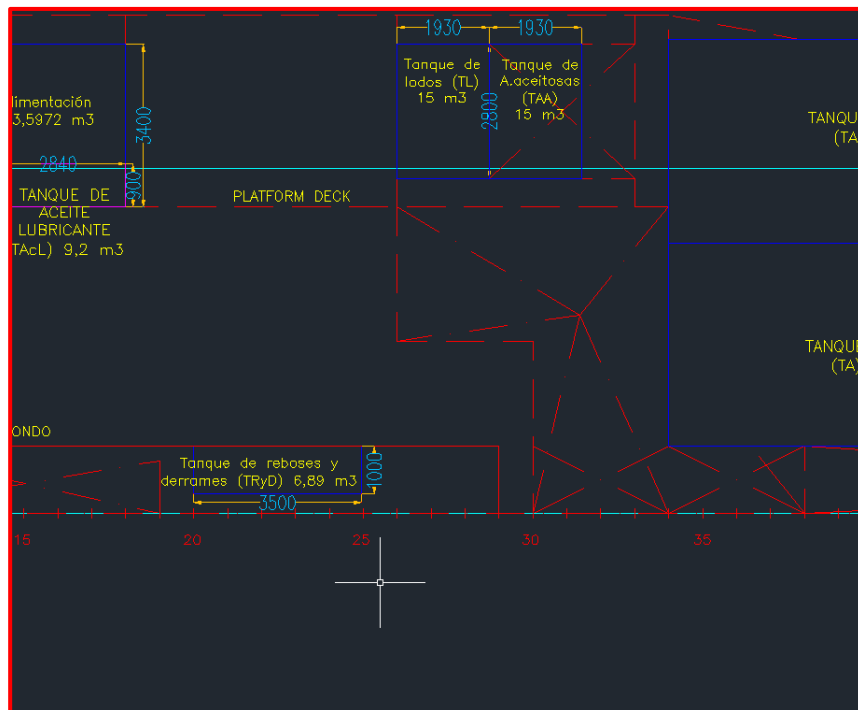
Tanques de reboses y derrames/ vista estribor (alzado)
